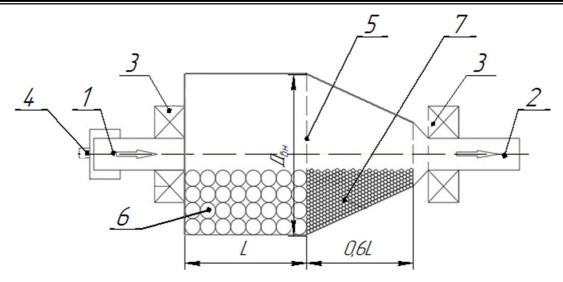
Схема шаровой мельницы: 1 – впускающий патрубок; 2 – выпускающий патрубок; 3 – подшипники качения; 4 – жиклер; 5 – решетка перфорированная; 6 – крупные шары; 7 – мелкие шары
